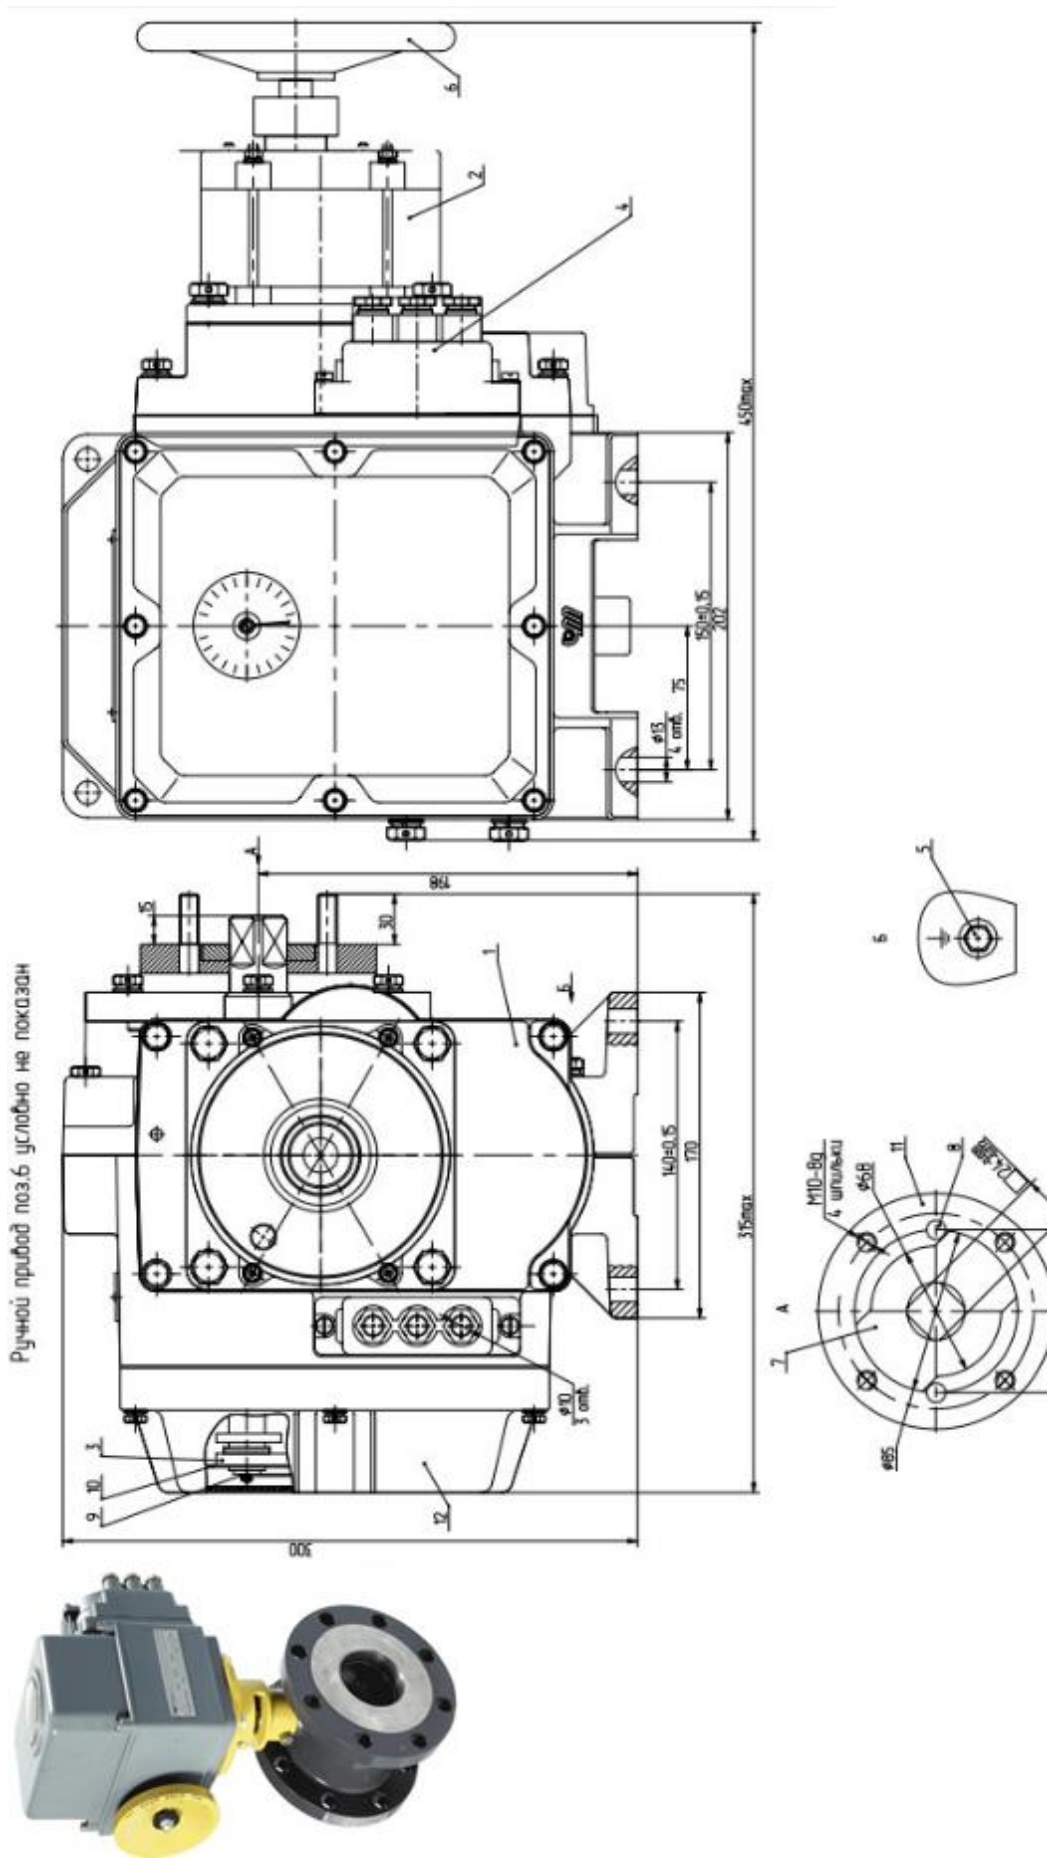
Исполнительный механизм однооборотный МЭО:
